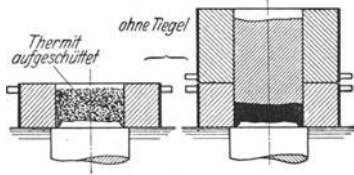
Thermit-Ausbesserungsschweißung.
